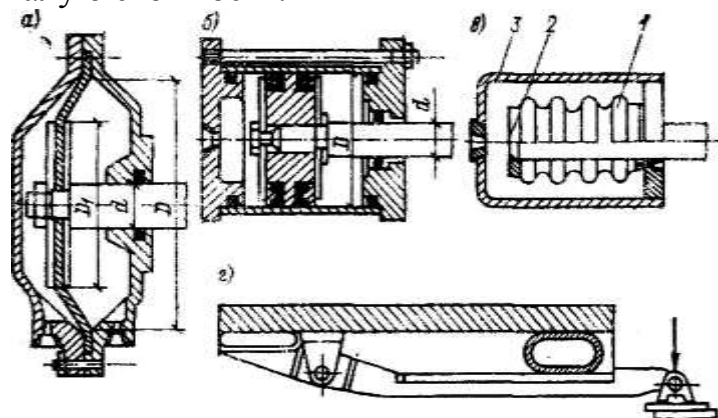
Типы пневмодвигателей: а — пневмокамера; б — пневмоцилиндр двустороннего действия; в — сильфон; г — пневмошланг; D — расчетный диаметр пневмопривода; D_1 — диаметр тарелки штока; d — диаметр штока; 1 — гофрированная камера; 2 — тарелка штока; 3 — наружная камера
